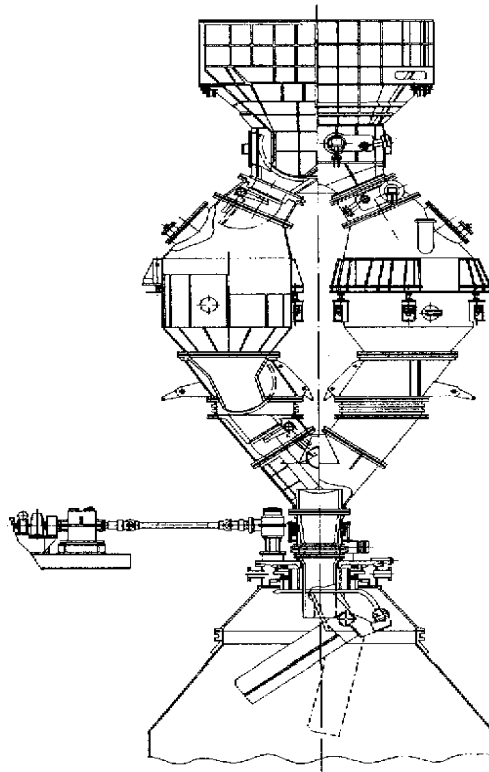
Безконусний завантажувальний пристрій конструкції
